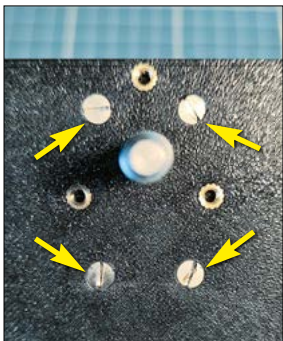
Motorbefestigung mit Senkkopfschrauben M3 x 8 mm; die Gewindebuchsen ...
